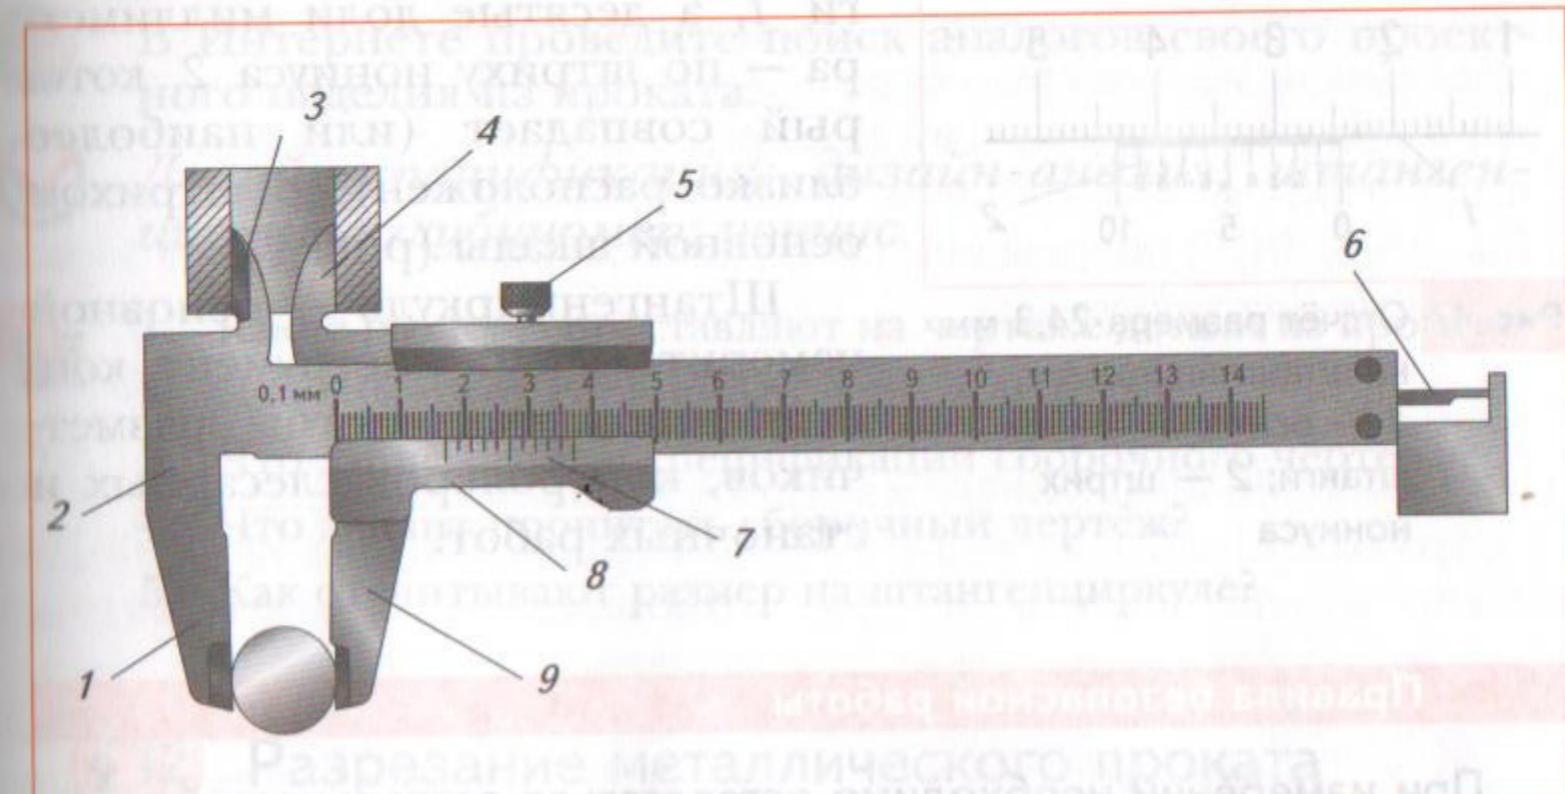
Устройство штангенциркуля: 1 — неподвижная нижняя измерительная губка; 2 — штанга; 3 — неподвижная верхняя измерительная губка; 4 — верхняя подвижная измерительная губка; 5 — зажимный винт; 6 — глубиномер; 7 — нониус; 8 — рамка; 9 — нижняя подвижная измерительная губка
